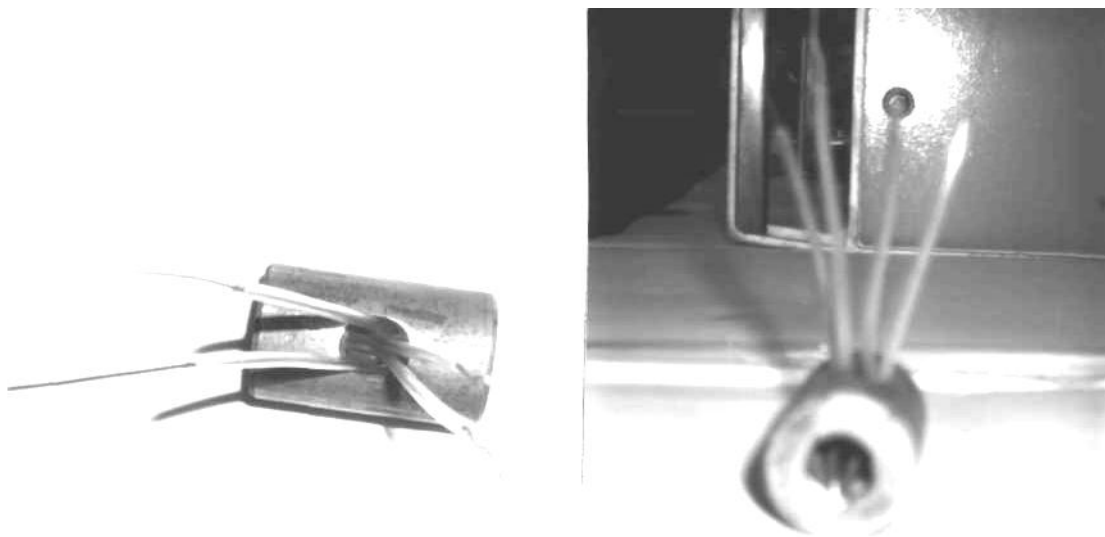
Заготовка со спаем термопар на торцах
